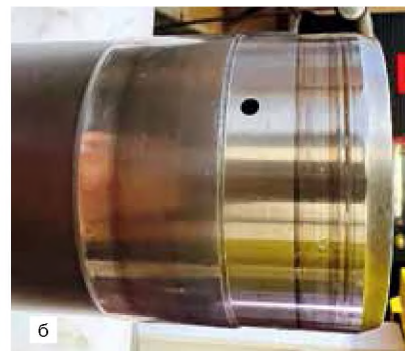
Ось привода цилиндрической прямозубой шестерни трактора «John Deere» с изношенным посадочным местом
